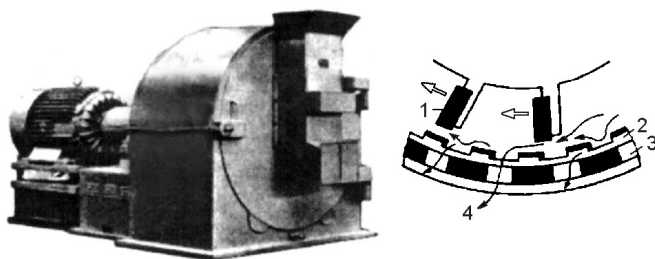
Схема работы и общий вид барабанной установки для доизмельчения стружки: 1 – лопасть, 2 – размольная дорожка, 3 – ситовое кольцо, 4 – крышка, 5 – лопастной ротор, 6 – корпус
